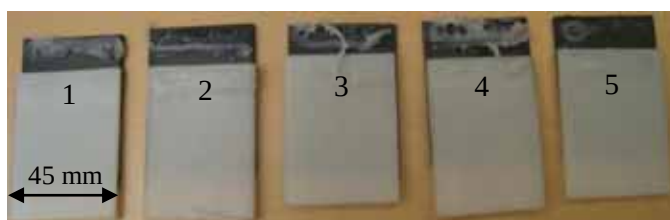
Corpos de prova da soldagem por vibração ensaiados por Lap Shear a 85°C
